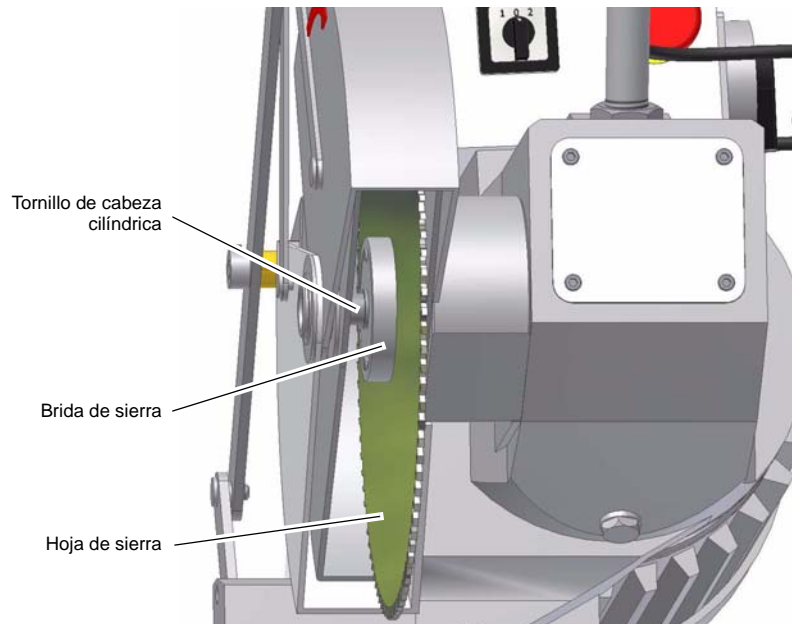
Montaje y cambio de la hoja de sierra
